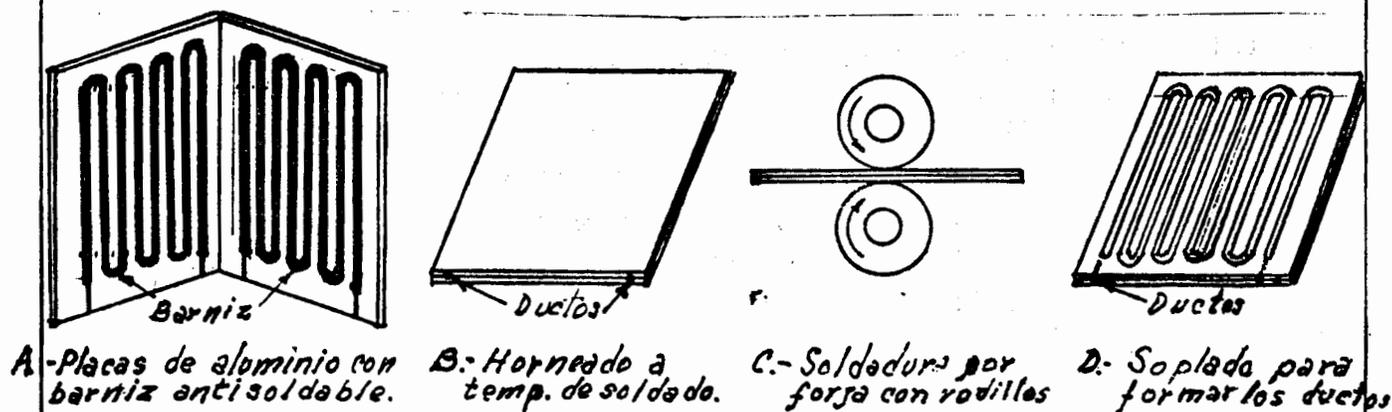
SOLDADURA CON RODILLOS APLICADA A LA FABRICACION DE EVAPORADORES PARA REFRIGERADOR.
